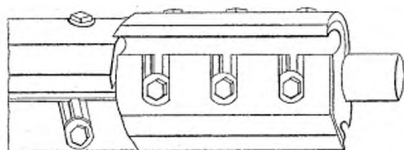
Porte-lames Humphreys pour machine à raboter.
